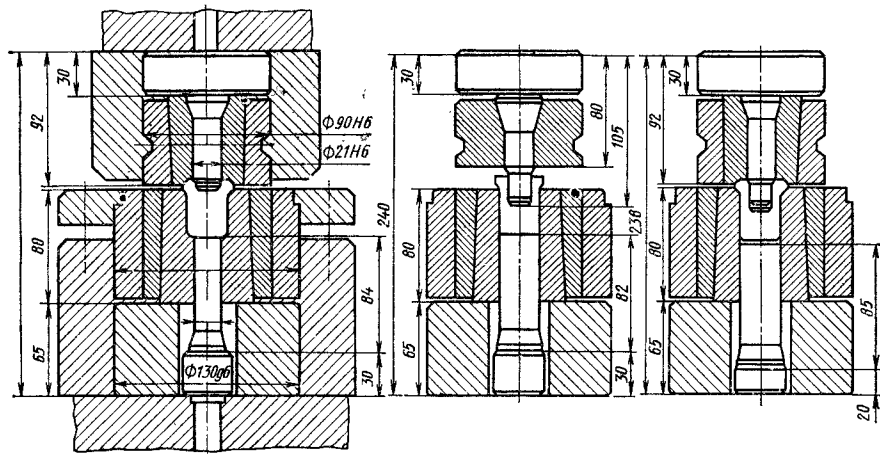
Наладка четырехпозиционного штампа для штамповки колпачковой гайки (см. рис. 53, в)
